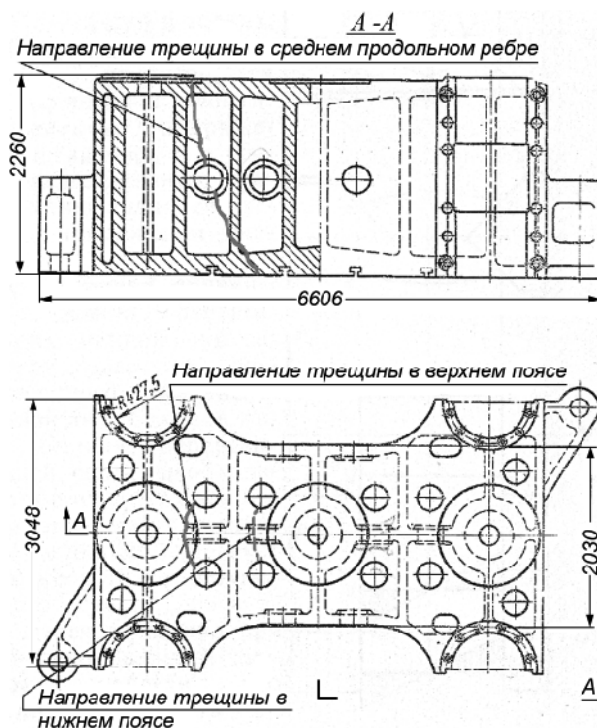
Трещина в ребре подвижной поперечины штамповочного пресса силой 100 МН
